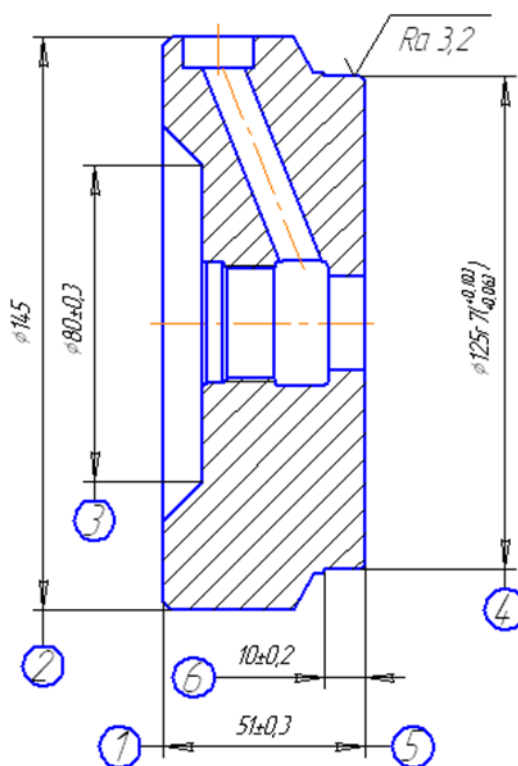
Эскиз детали «Крышка цилиндра»
